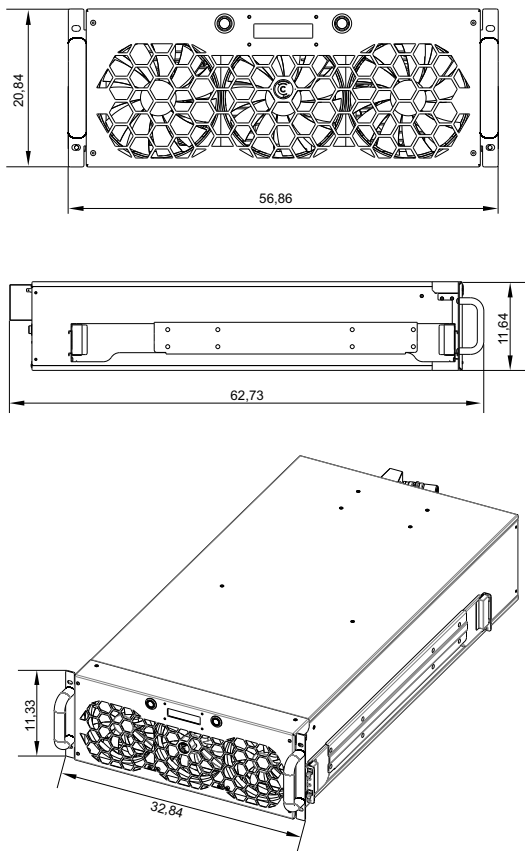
Габаритные размеры драйкулера / Figure 1 – Overall dimensions of the dry cooler
